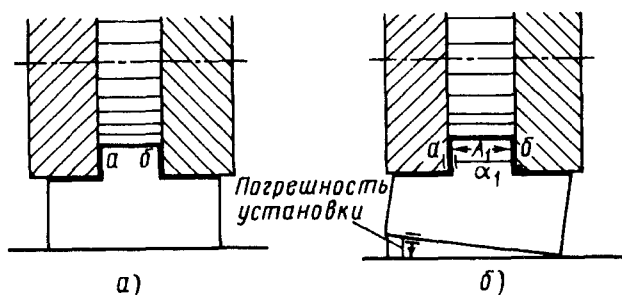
Схема обработки детали, показывающая, что погрешность установки не влияет на точность относительного положения поверхностей детали, обработанных с одной установки:
